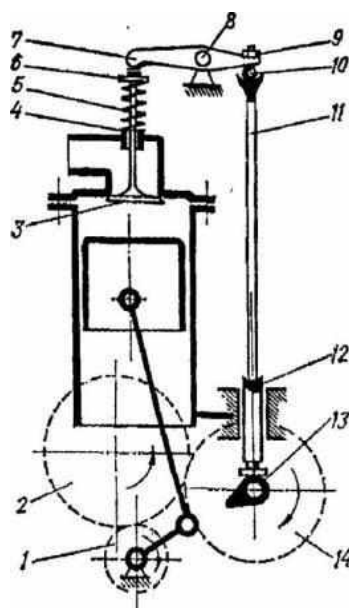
Схема клапанного механізму газорозподілу:
